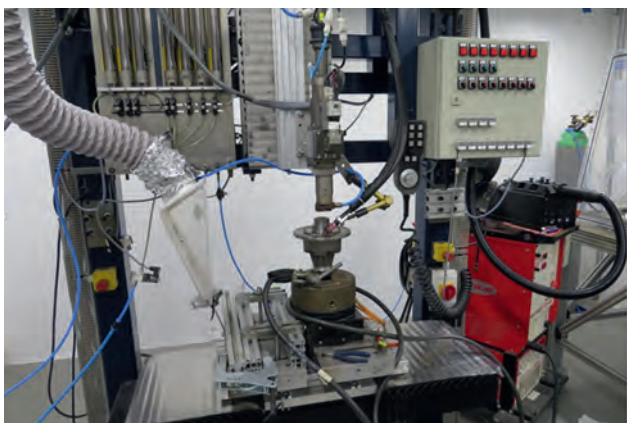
Laser Schweißanlage mit beheiztem Schweißdraht
